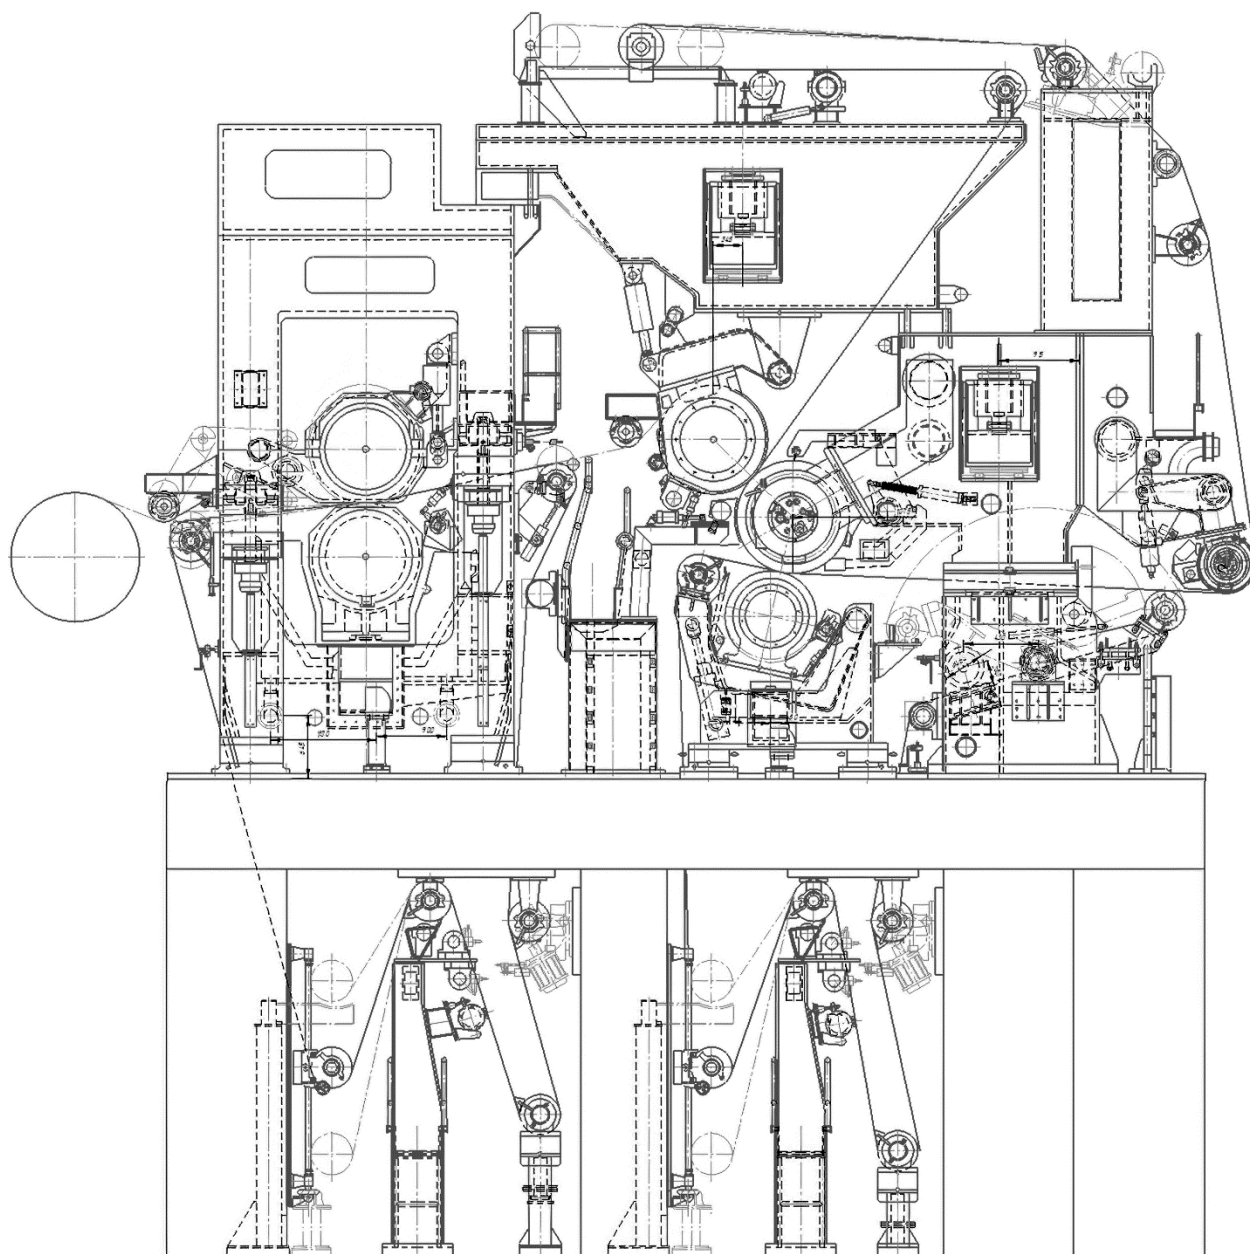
Прессовая часть с валами обычной конструкции, Сыктывкарский ЦБК
